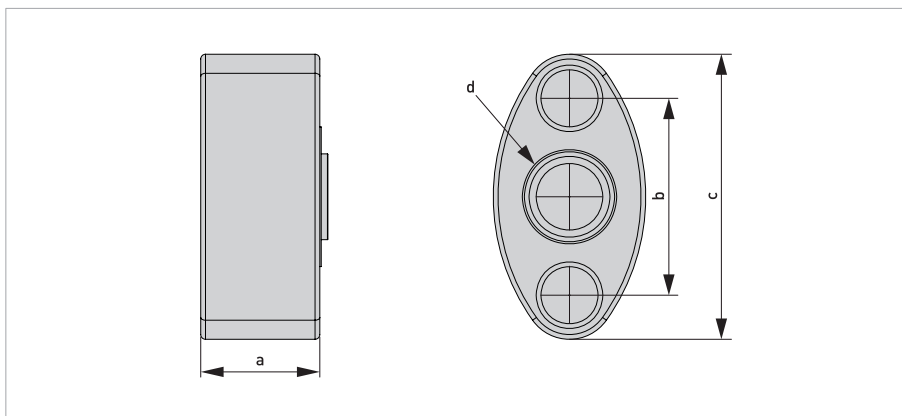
Овальный фланцевый адаптер (Ах)
